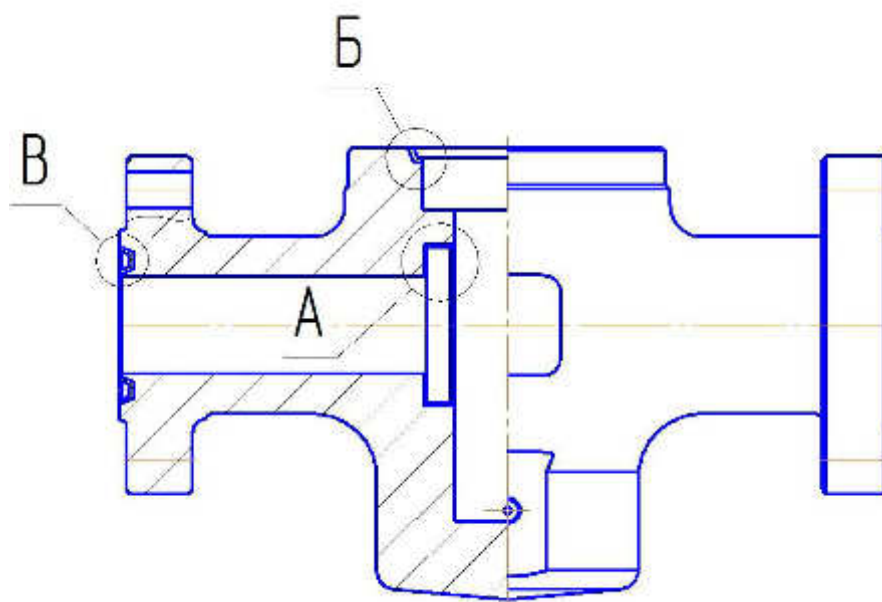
Наплавляемые поверхности корпуса задвижки
